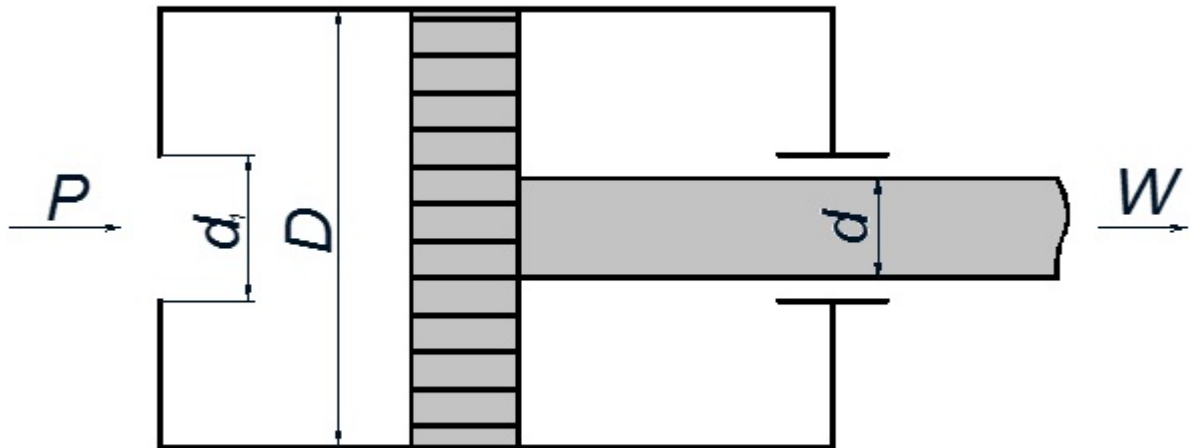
Розрахункова схема пневмоциліндра
